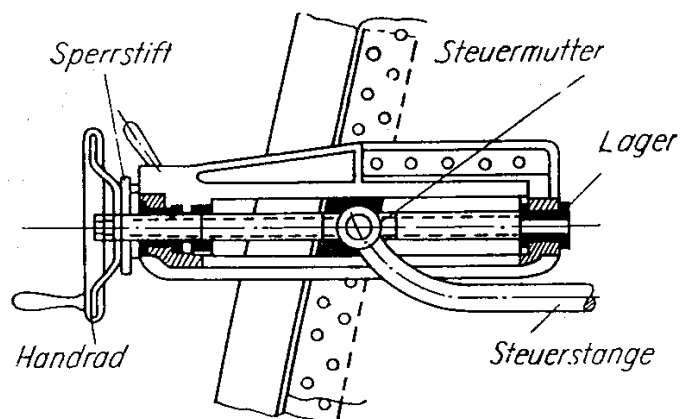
Steuerbock mit Schraube für Einheitslokomotiven der Deutschen Reichsbahn
